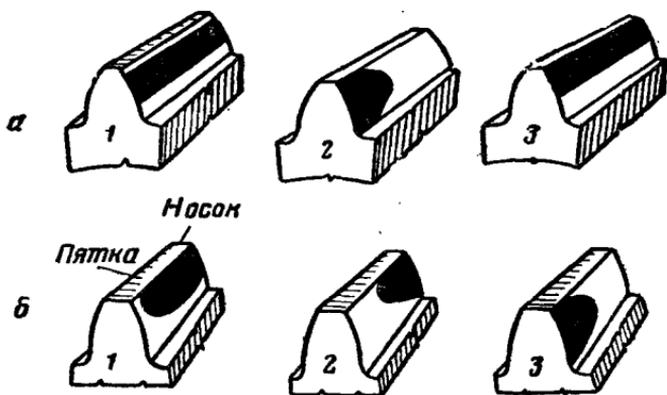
Отпечатки следов зацепления зубчатых колес:
